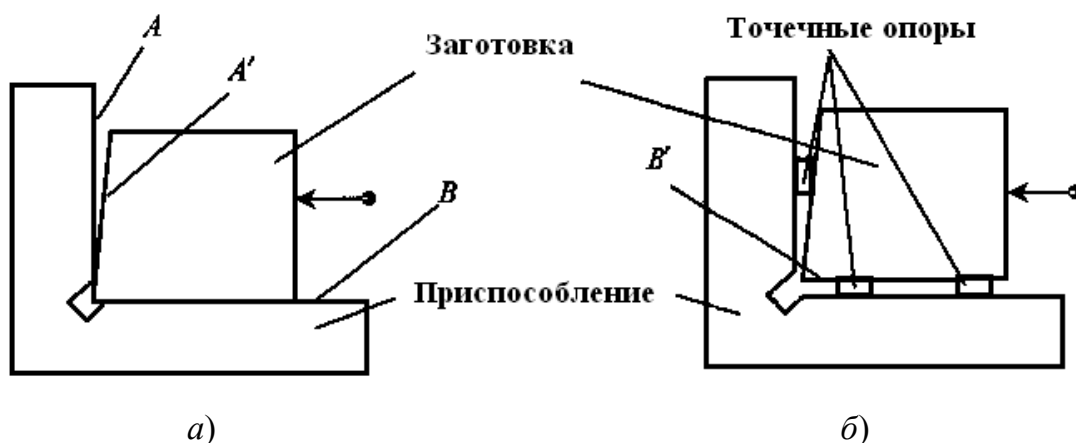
Схема установки призматической заготовки в приспособление:
